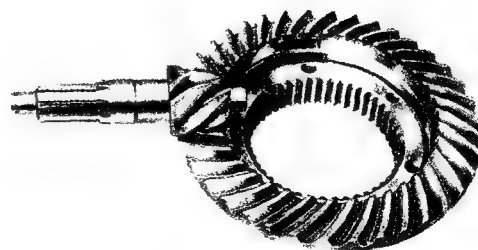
Juego de engranajes con dentado en espiral (Demm).
